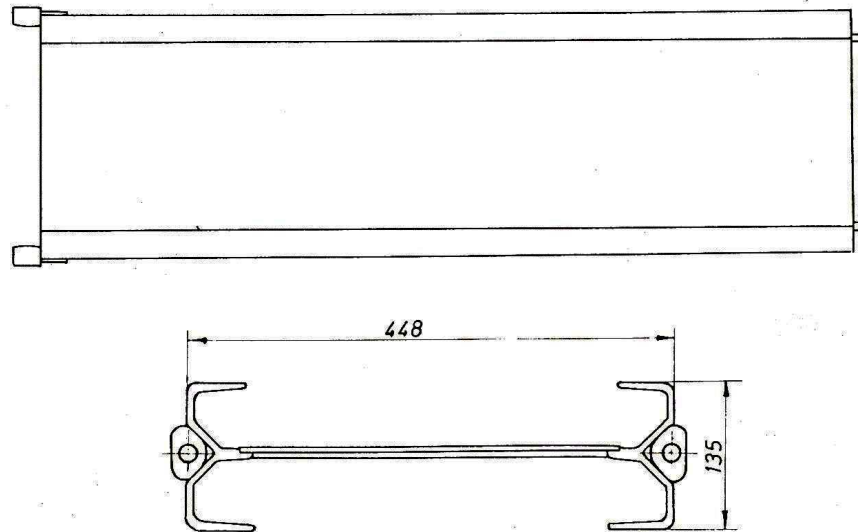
Alzado, perfil y planta del transportador blindado
